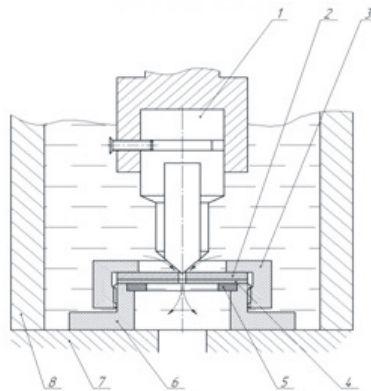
б. - 1-ЕІ; 2-заготовка; 3-притисна гайка; 4-підкладка; 5-прокладка; 6-фланець; 7-підкладна плита; 8-гідрокамера
